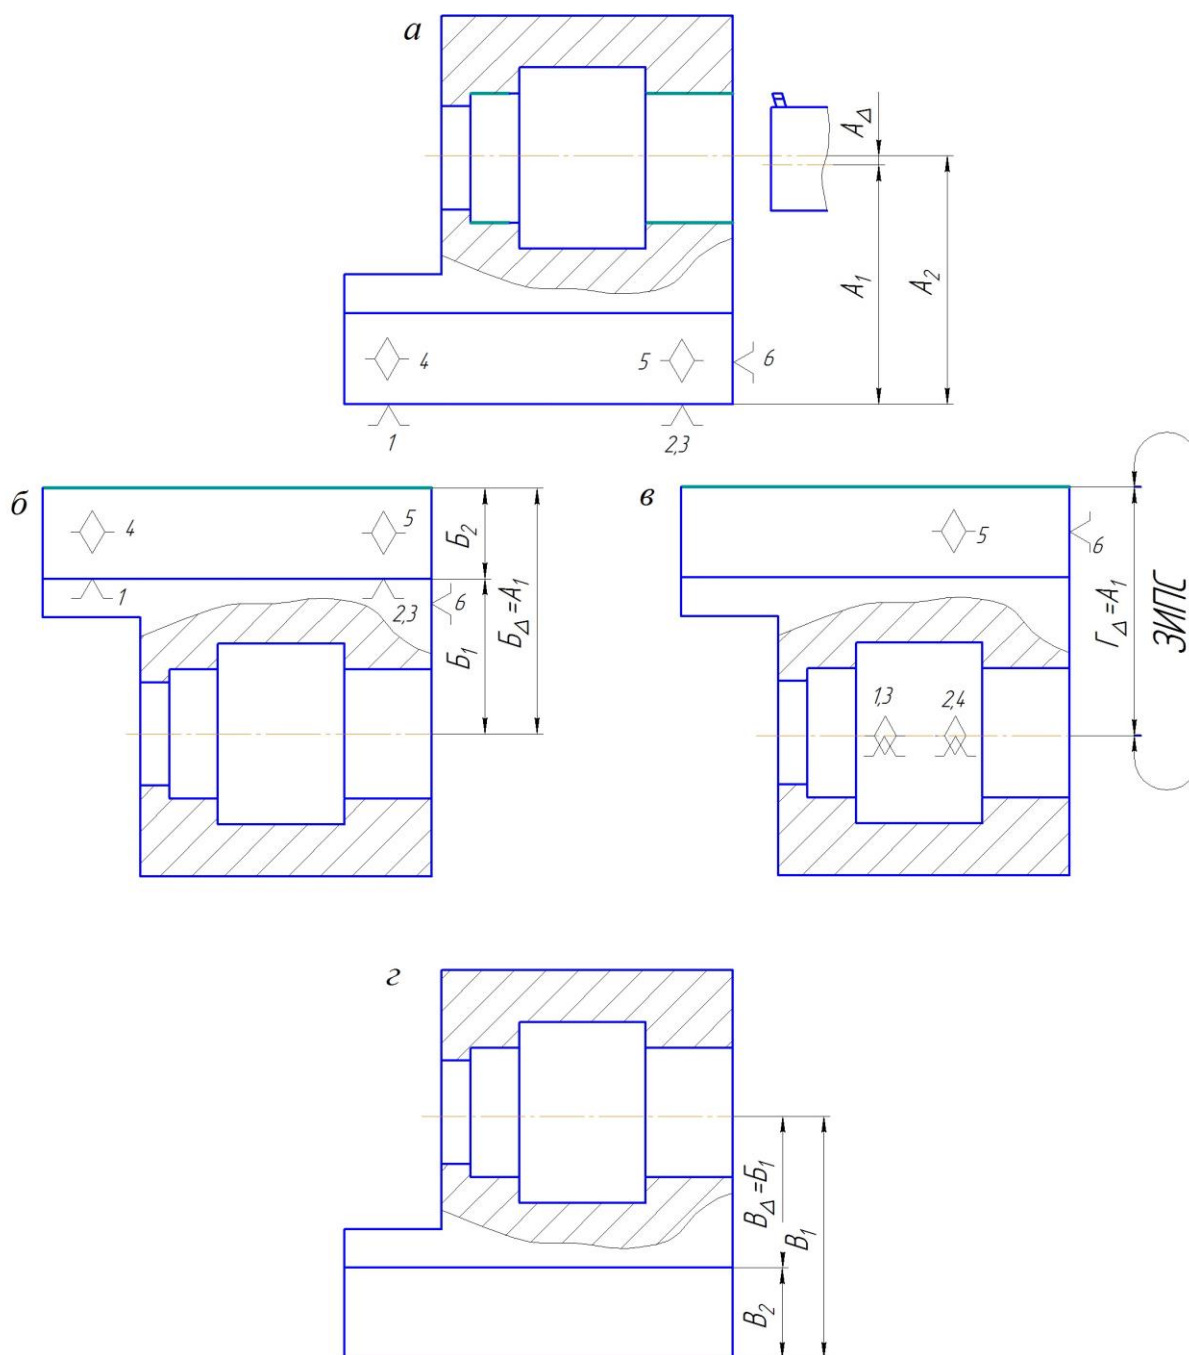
Схемы базирования и эскиз заготовки:
